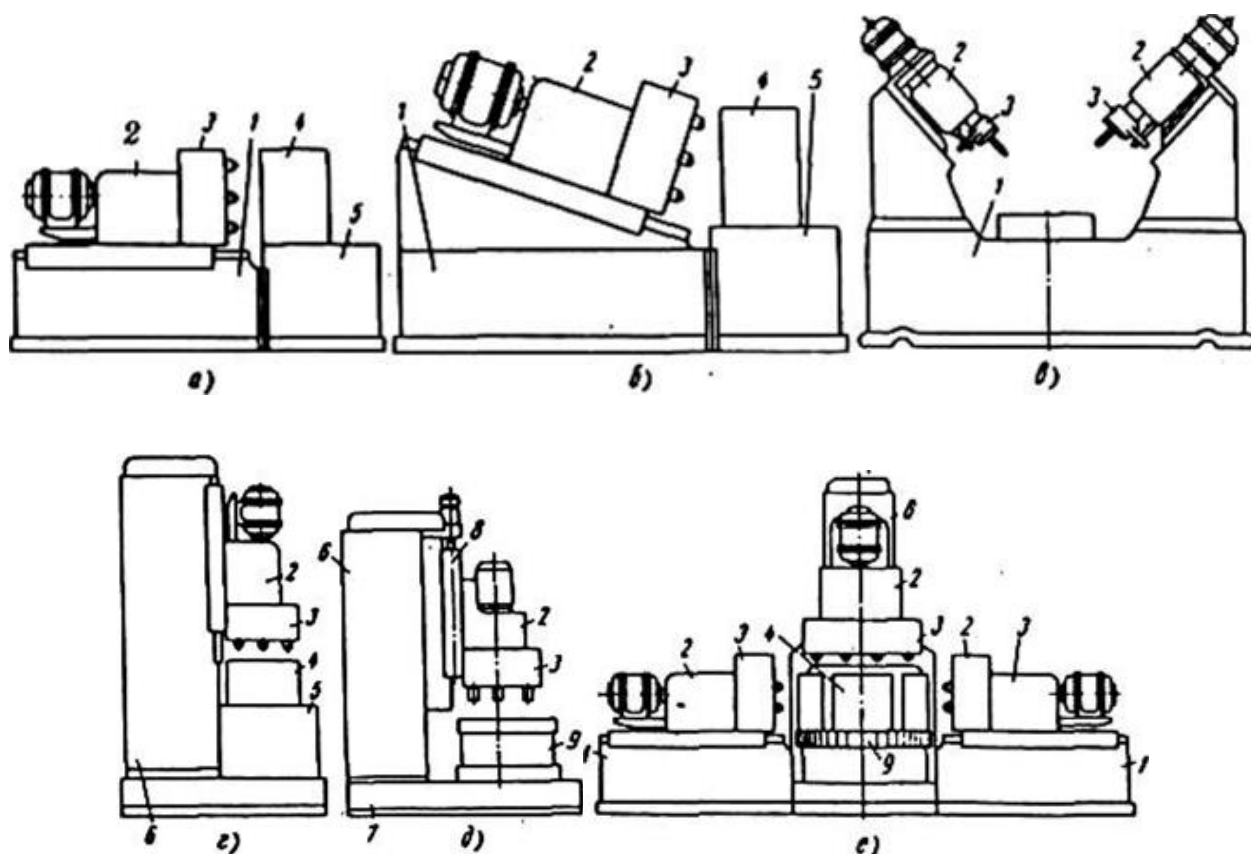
Схеми компонування агрегатних верстатів
